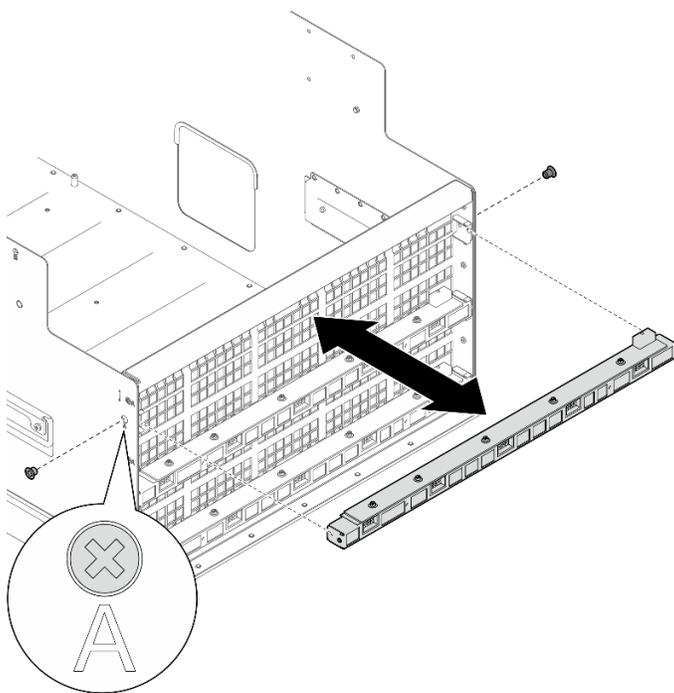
Instalação do conjunto placa de controle do ventilador traseiro
